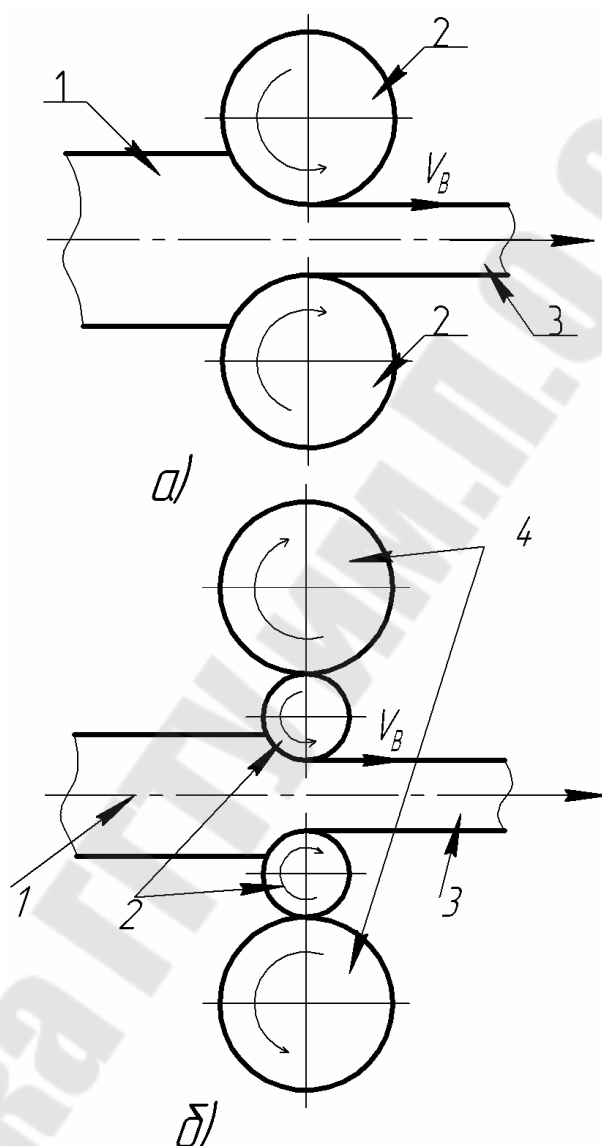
Схемы продольной прокатки: *а* – двухвалковая прокатка: 1 – заготовка; 2 – прокатные валки; 3 – прокат; V_B – вектор линейной скорости вращения валков; *б* – четырехвалковая прокатка: 1 – заготовка; 2 – прокатные валки; 3 – прокат; 4 – опорные валки; V_B – вектор линейной скорости вращения валков
